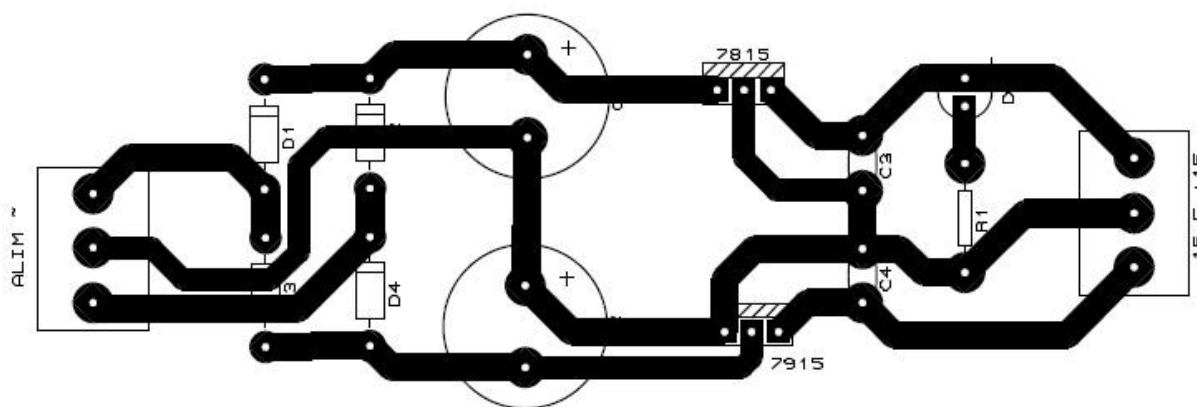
Layout Fonte Simétrica. Fonte [Autor].
